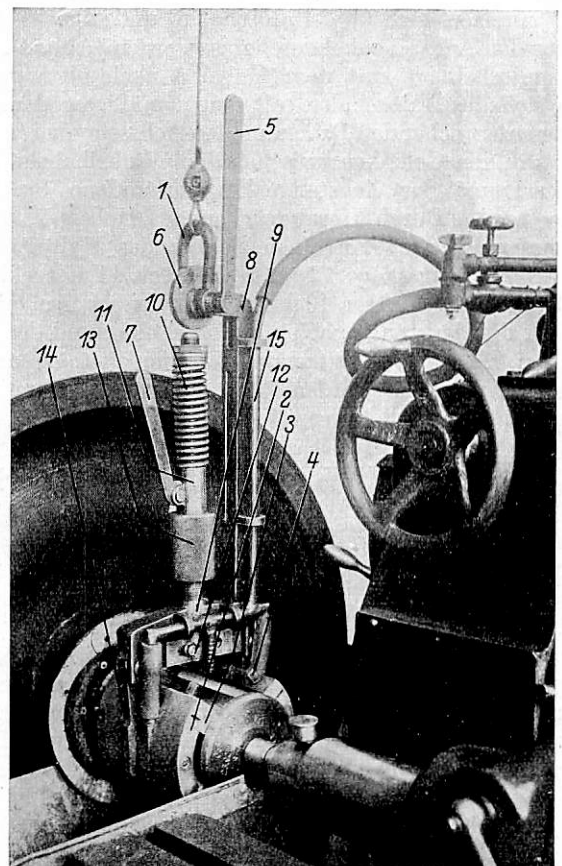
Zieh schleifwerkzeug an einer Achsschenkel schleifmaschine. Werkzeug auf den Achsschenkel aufgesetzt.
